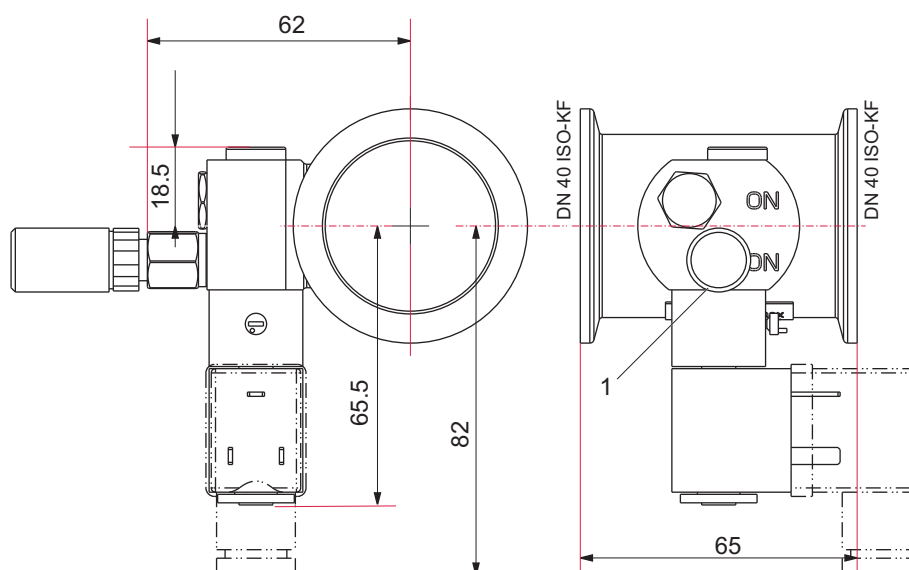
Magnetventil Lufteinlass – Abmessungen
